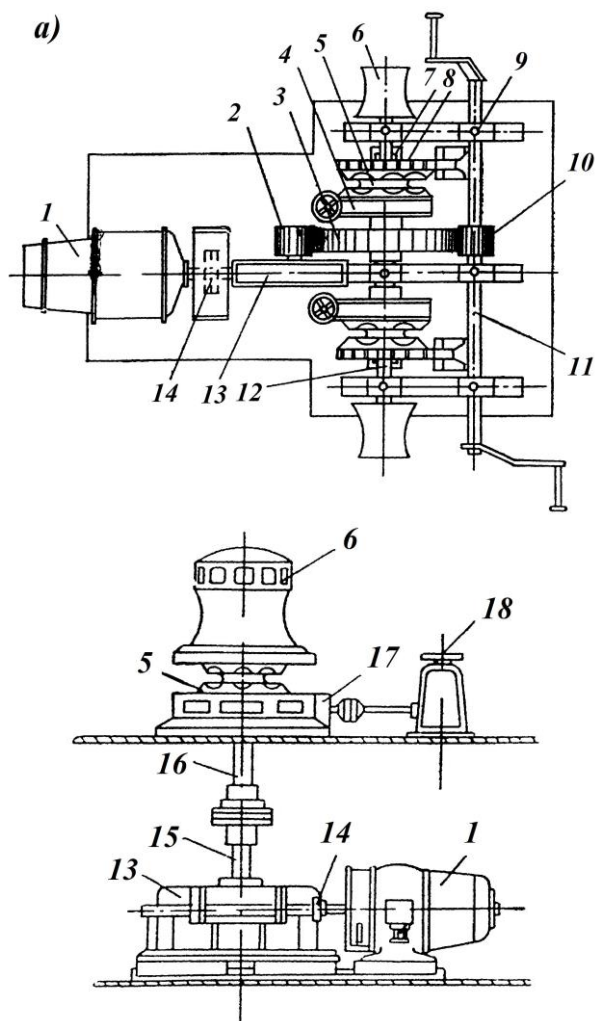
Якорные механизмы: *а* – брашпиль, *б* – шпиль; 1 – электродвигатель; 2, 3, 10 – цилиндрические шестерни; 4 – ленточный тормоз, 5 – цепная звездочка, 6 – швартовый барабан (турачка), 7 – кулачковая муфта, 8 – храповое колесо, 9 – собачка храпового колеса, 11 – вал ручного привода, 12 – вал цепных звездочек, 13 – червячная передача, 14 – муфта соединительная, 15 – вертикальный вал, 16 – баллер шпилья, 17 – колодочный тормоз, 18 – привод тормоза
